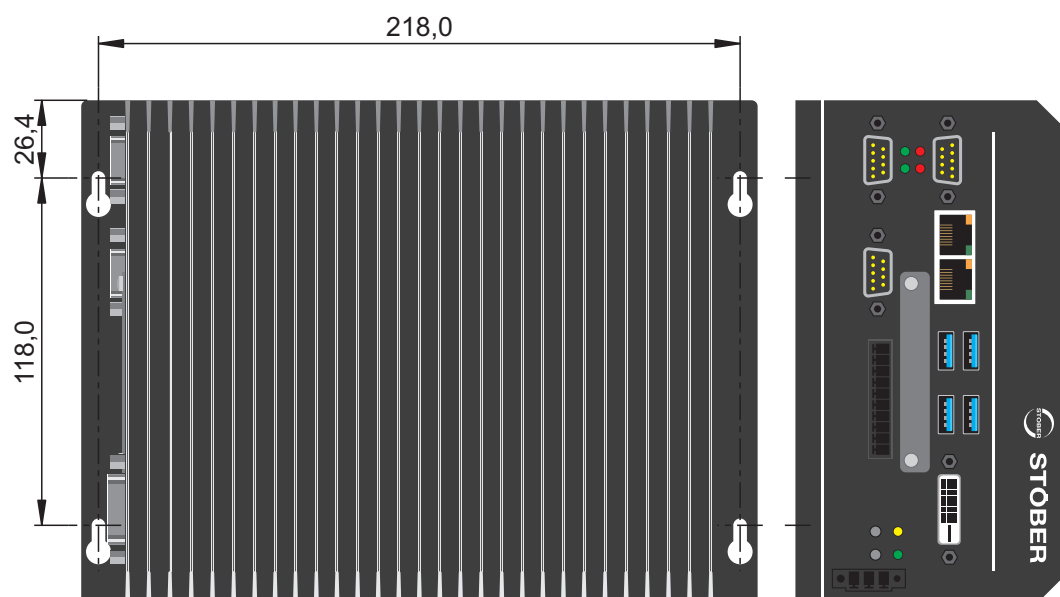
Plan de perçage (toutes les dimensions en mm)
